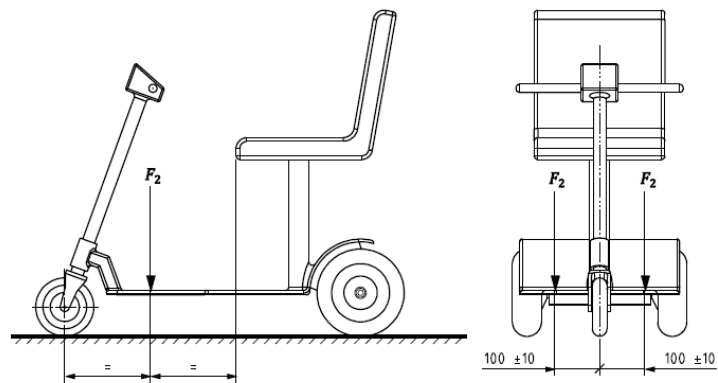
Ubicación de las cargas de apoyo para los pies (aplicadas por separado) en escúter
